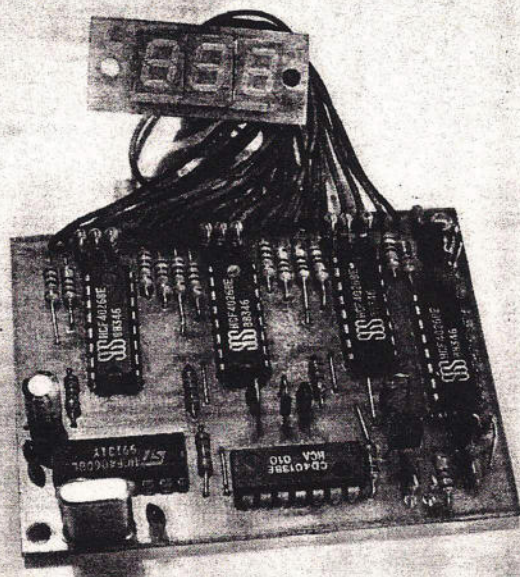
Der Zähler gleicht in seinen Abmessungen dem „Mini“-RX
